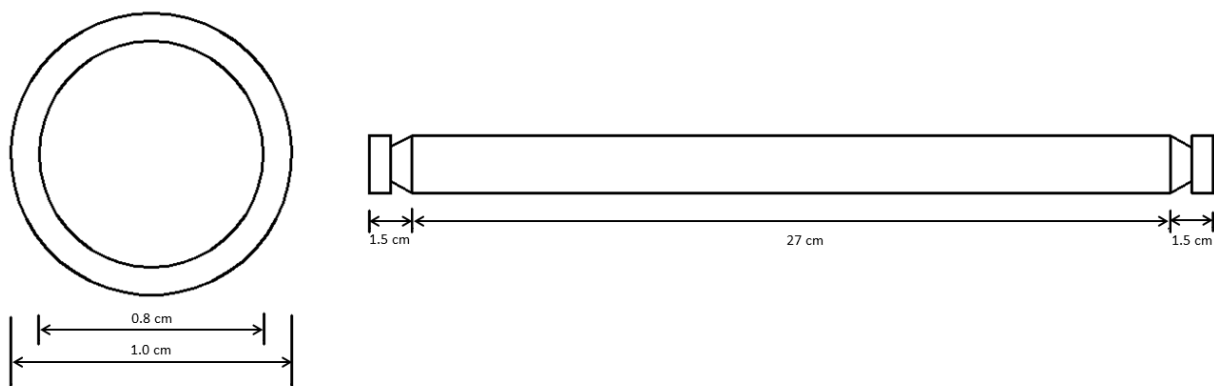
Vistas transversal y longitudinal de la columna de 8 mm de diámetro.
